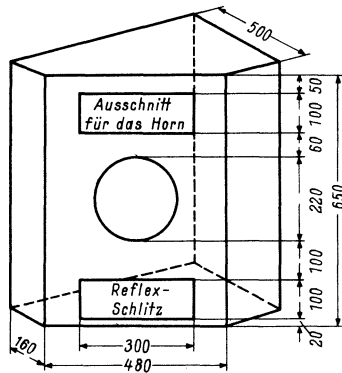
Maßskizze der Eckbox, alle Maße in Millimetern
